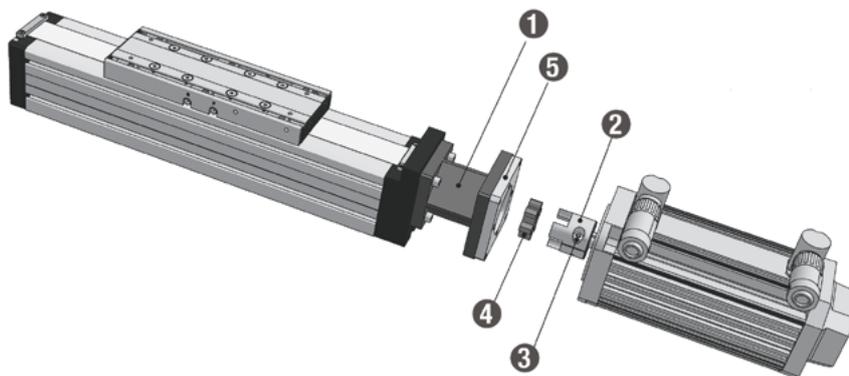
Motormontage an Linearachsen mit Spindeltrieb und Kupplungsglocke
